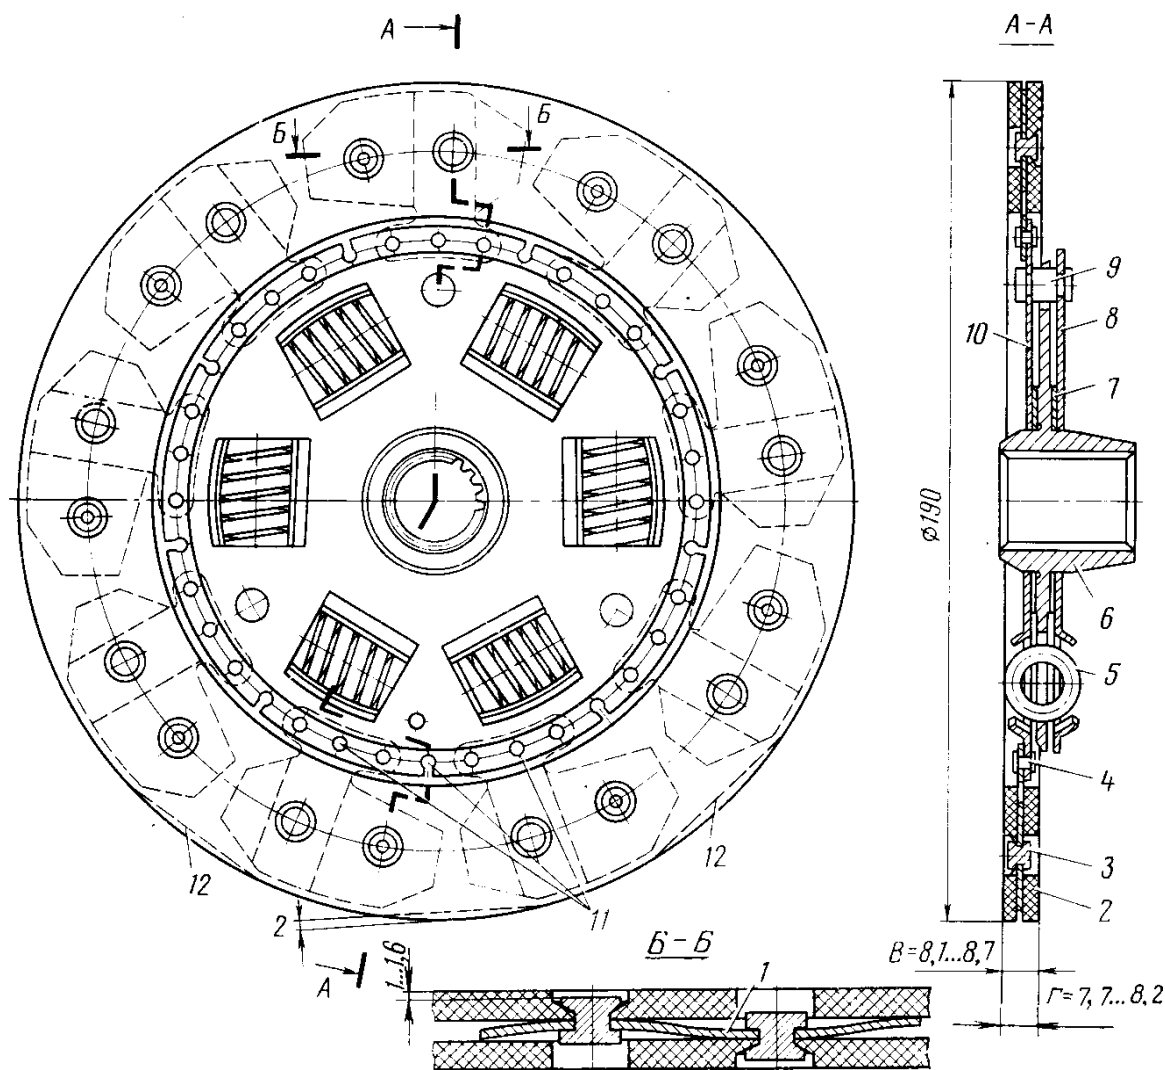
Ведомый диск сцепления в сборе: 1 — пружинная пластина; 2 — фрикционная накладка; 3, 4 — заклепки; 5 — пружина демпфера; 6 — ступица; 7 — кольцо демпфера; 8 — пластина демпфера; 9 — палец; 10 — ведомый диск; 11 — место установки балансировочных грузиков; 12 — места снятия материала фрикционных накладок при статической балансировке;
